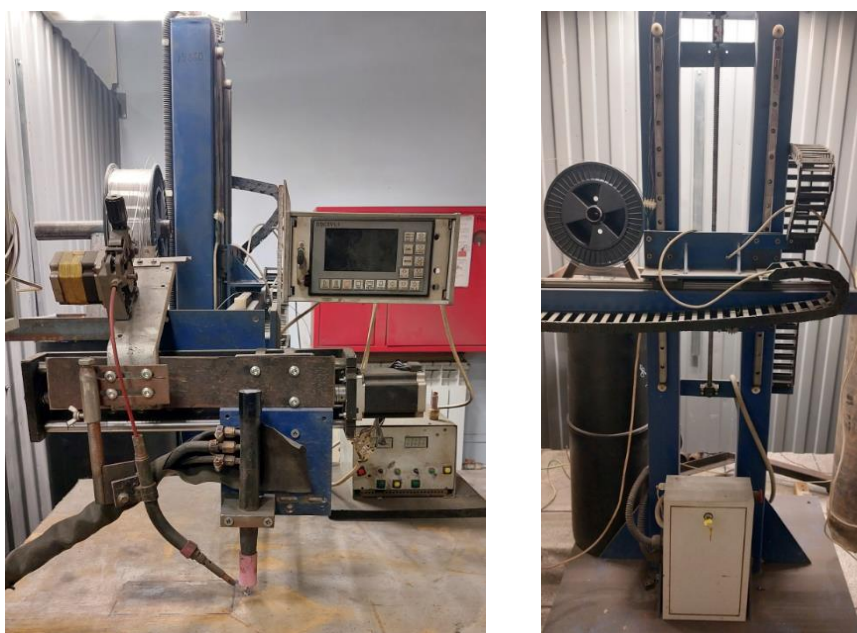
Внешний вид сварочной колонны
